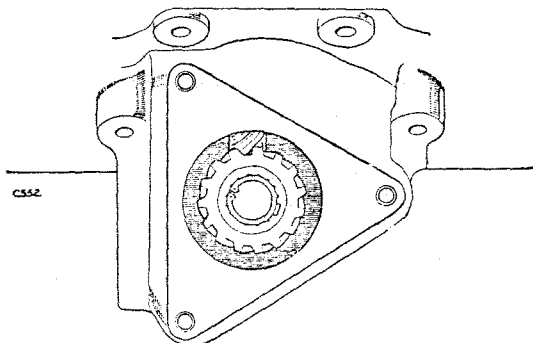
Engranaje de transmisión en la posición correcta de puesta a punto.
